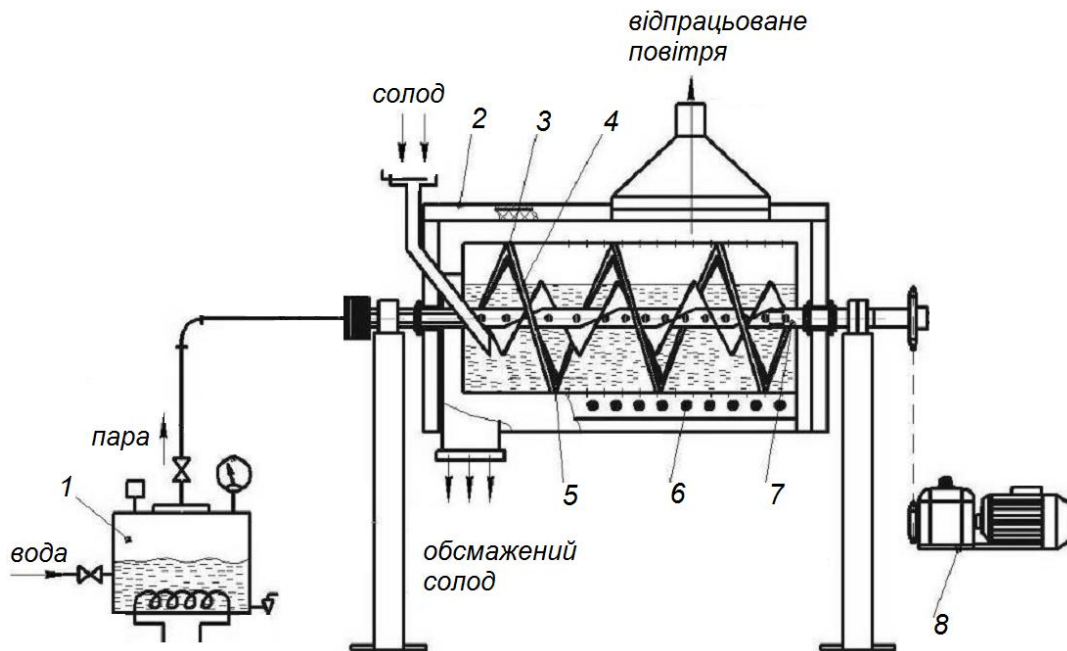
Структурна схема розробленого обсмажувача солоду: 1 – генератор пари; 2 – корпус станини; 3 – барабан; 4 – лопатки барабана; 5 – кожух барабана; 6 – трубчасті електронагрівачі; 7 – порожнистий вал внутрішнього шнека; 8 – редуктор із електродвигуном.
